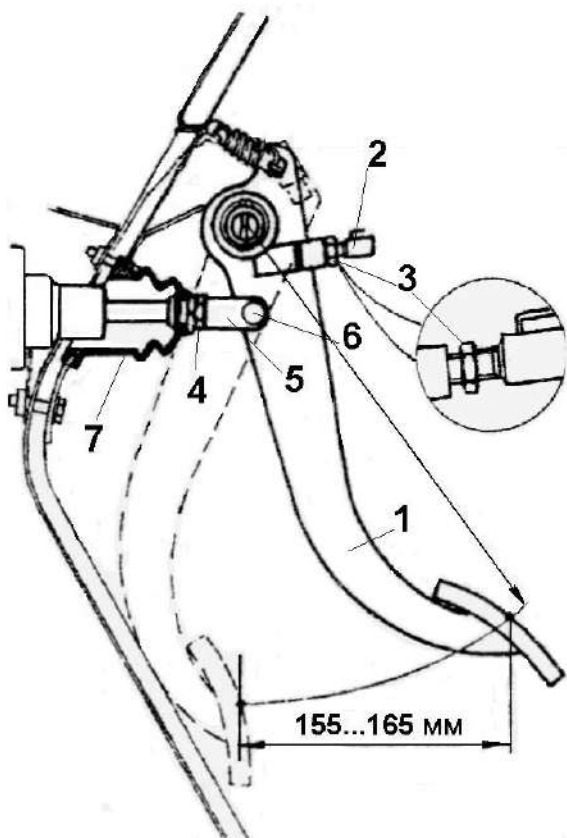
Схема проверки хода педали тормоза: 1- педаль тормоза; 2- выключатель сигнала торможения; 3- контрагайка выключателя; 4- контрагайка толкателя; 5- толкатель с вилкой в сборе; 6- палец вилки; 7-пыльник резиновый;
